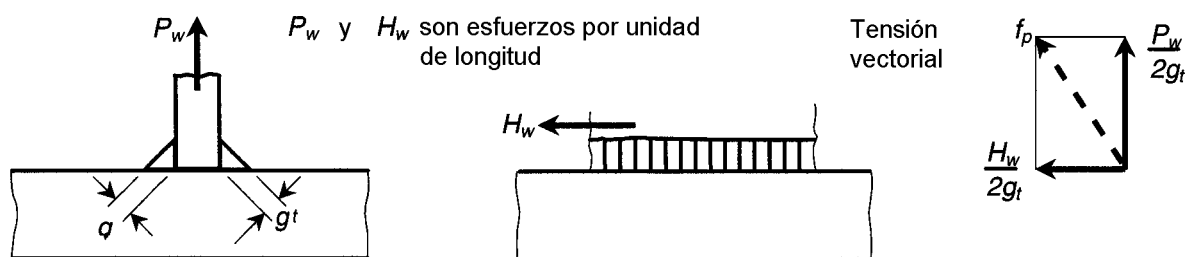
Tensiones en gargantas de soldaduras
